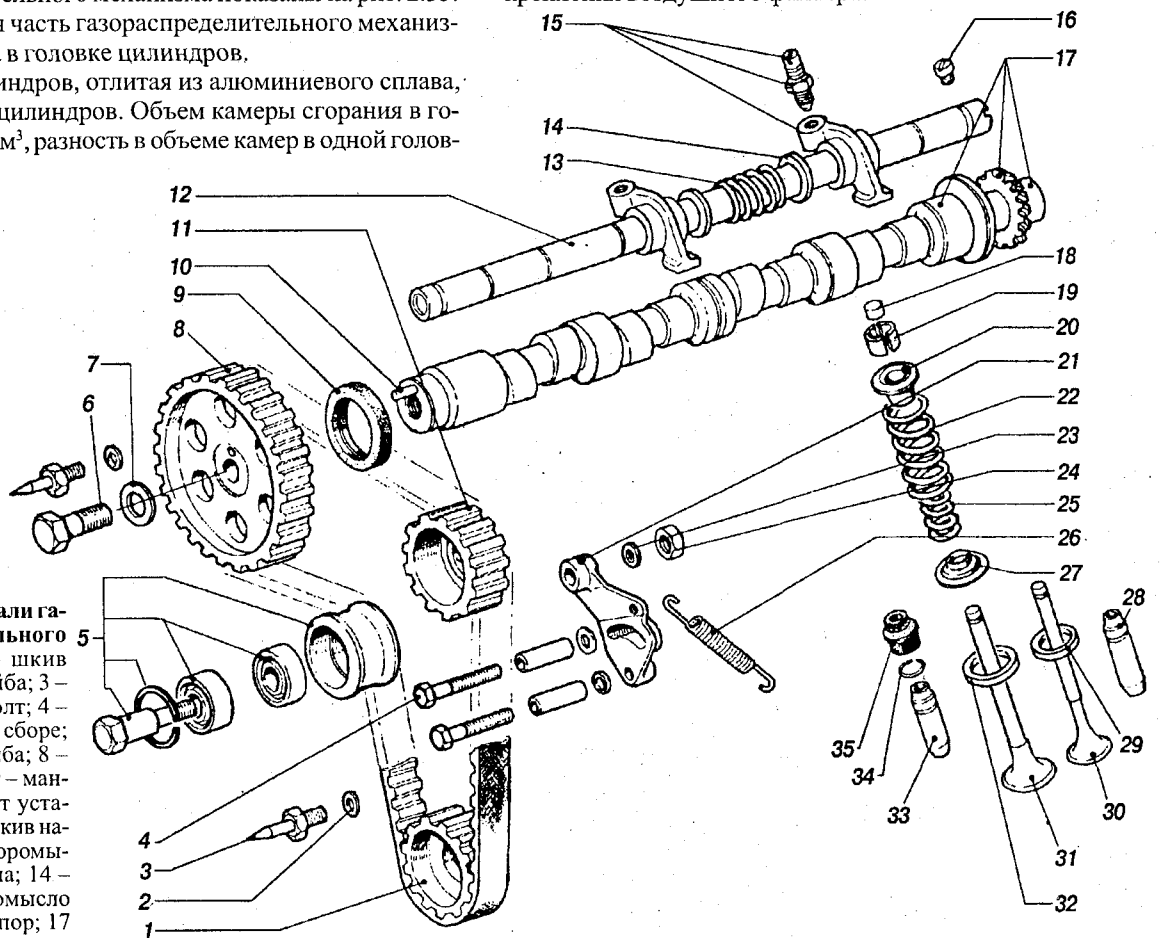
Детали газораспределительного механизма. 1 – шкив ведущий; 2 – шайба; 3 – установочный болт; 4 – болт; 5 – ролик в сборе; 6 – болт; 7 – шайба; 8 – шкив ведомый; 9 – манжета; 10 – штифт установочный; 11 – шкив насоса; 12 – ось коромысел; 13 – пружина; 14 – шайба; 15 – коромысло в сборе; 16 – стопор; 17 – вал распределительный в сборе; 18 – наконечник; 19 – сухарь; 20 – тарелка; 21 – кронштейн; 22 – пружина наружная; 23 – шайба; 24 – гайка; 25 – пружина внутренняя; 26 – пружина; 27 – шайба опорная; 28 – втулка выпускного клапана; 29 – седло выпускного клапана; 30 – выпускной клапан; 31 – впускной клапан; 32 – седло впускного клапана; 33 – втулка впускного клапана с кольцом; 34 – стопорное кольцо; 35 – маслоотражательный колпачок
